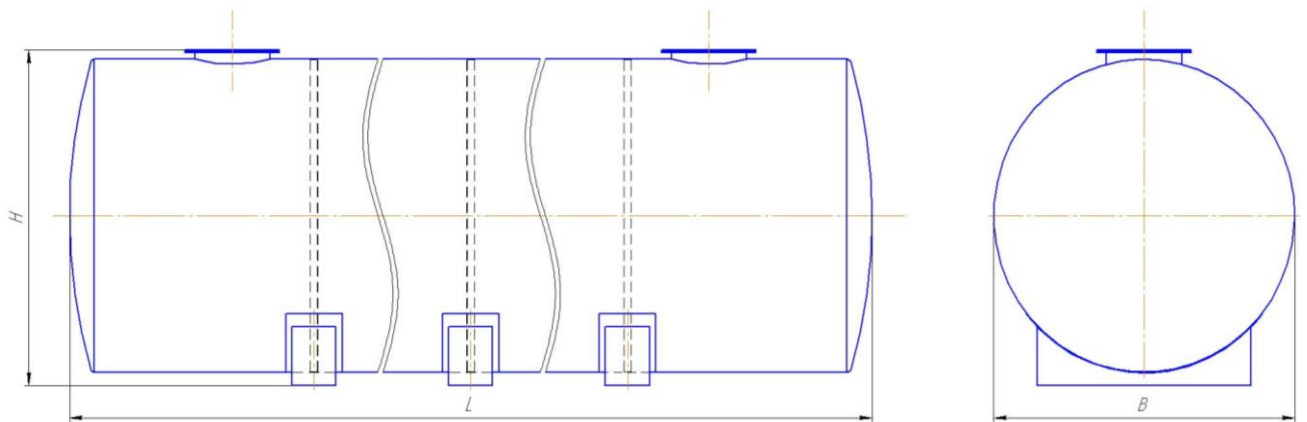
Горизонтальный резервуар, многокамерный с сферическими днищами.
